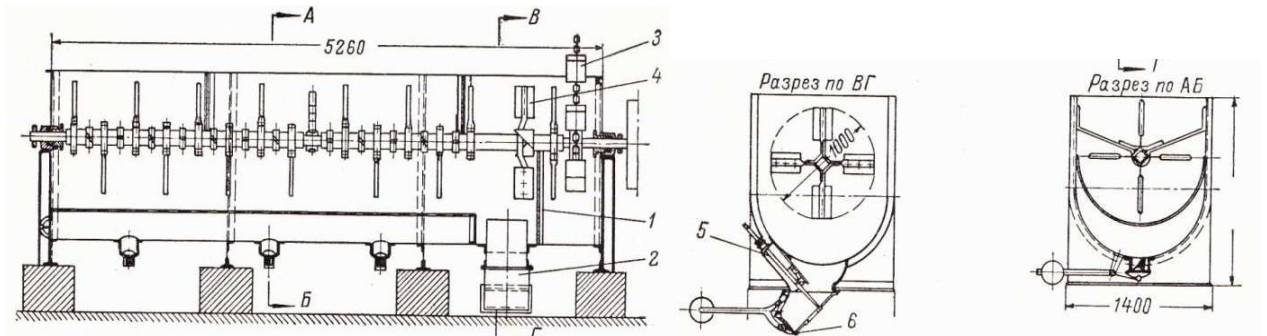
Схема кулачкової коренебульбоплодної мийної машини з металевою односекційною ванною і каменеуловлювачем: 1 - перегородка; 2 - каменеуловлювач; 3 - ковшовий транспортер; 4 - викидають черпаки; 5 - засувка; 6 - люк для вивантаження каменів
